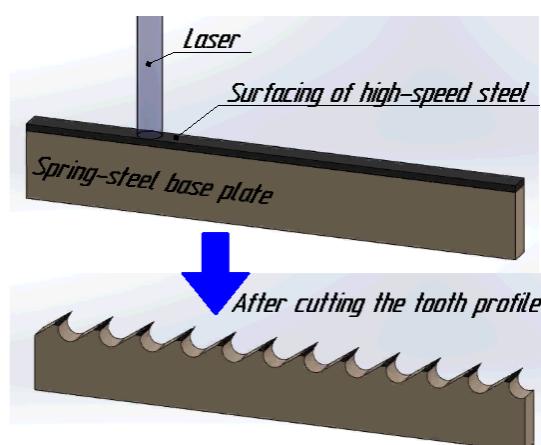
Производство биметаллических режущих инструментов с использованием технологии лазерной сварки
